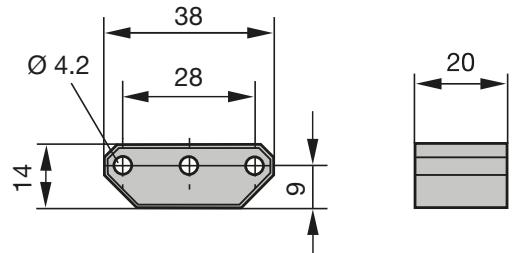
Dimensions de montage du capteur de position BTL5-P-3800-2
